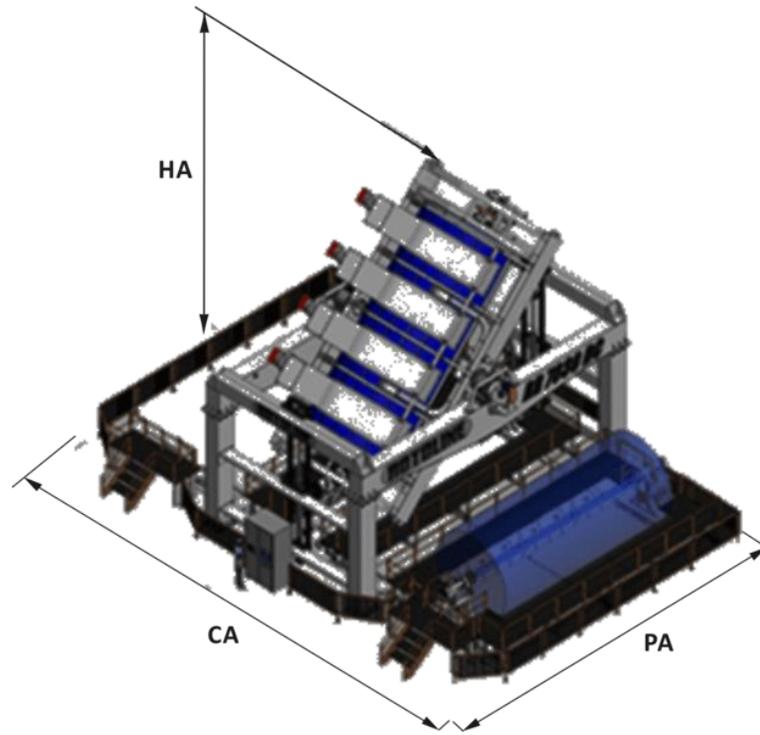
Máquina de rotomoldeo tipo rock & roll. [62]
